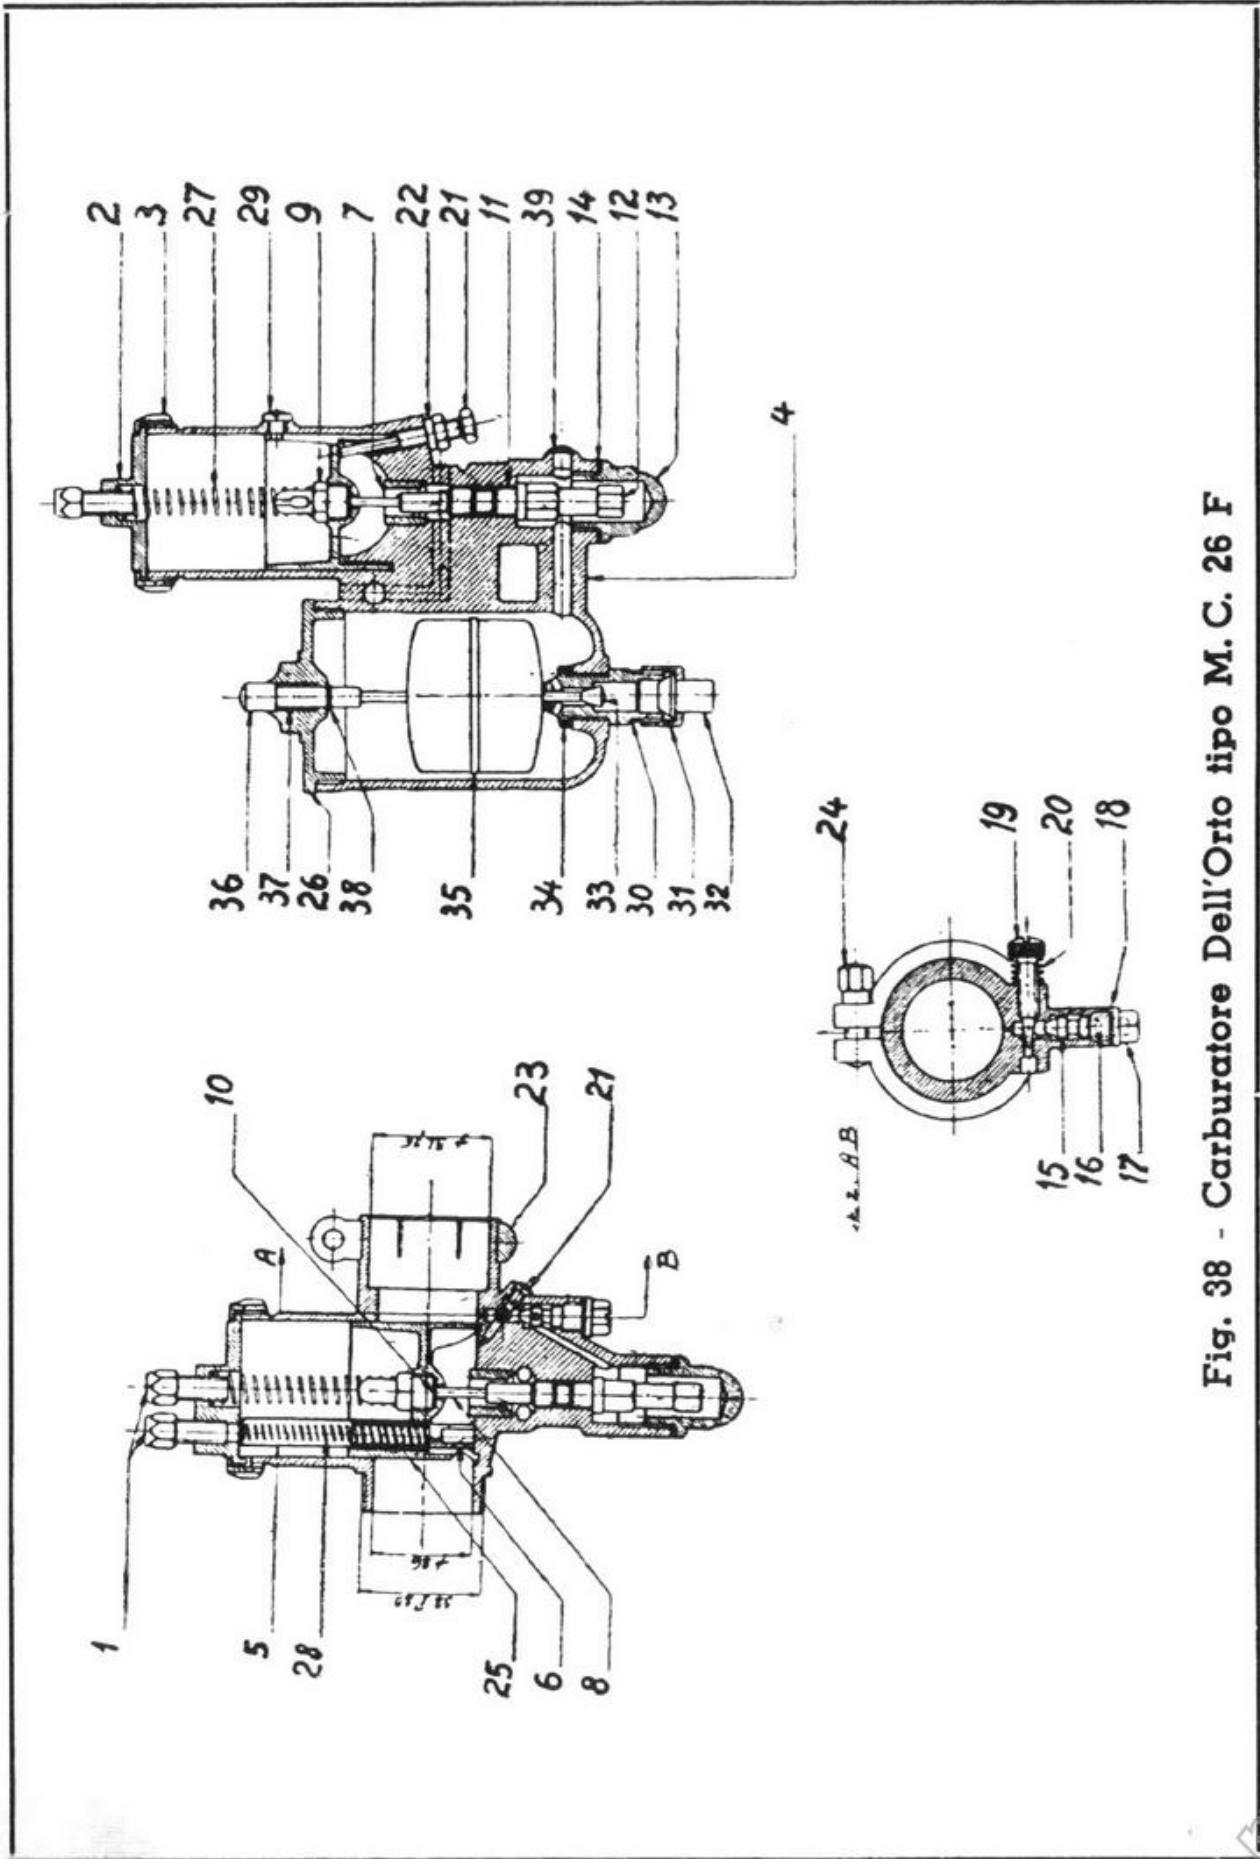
Carburatore Dell'Orto tipo M. C. 26 F
